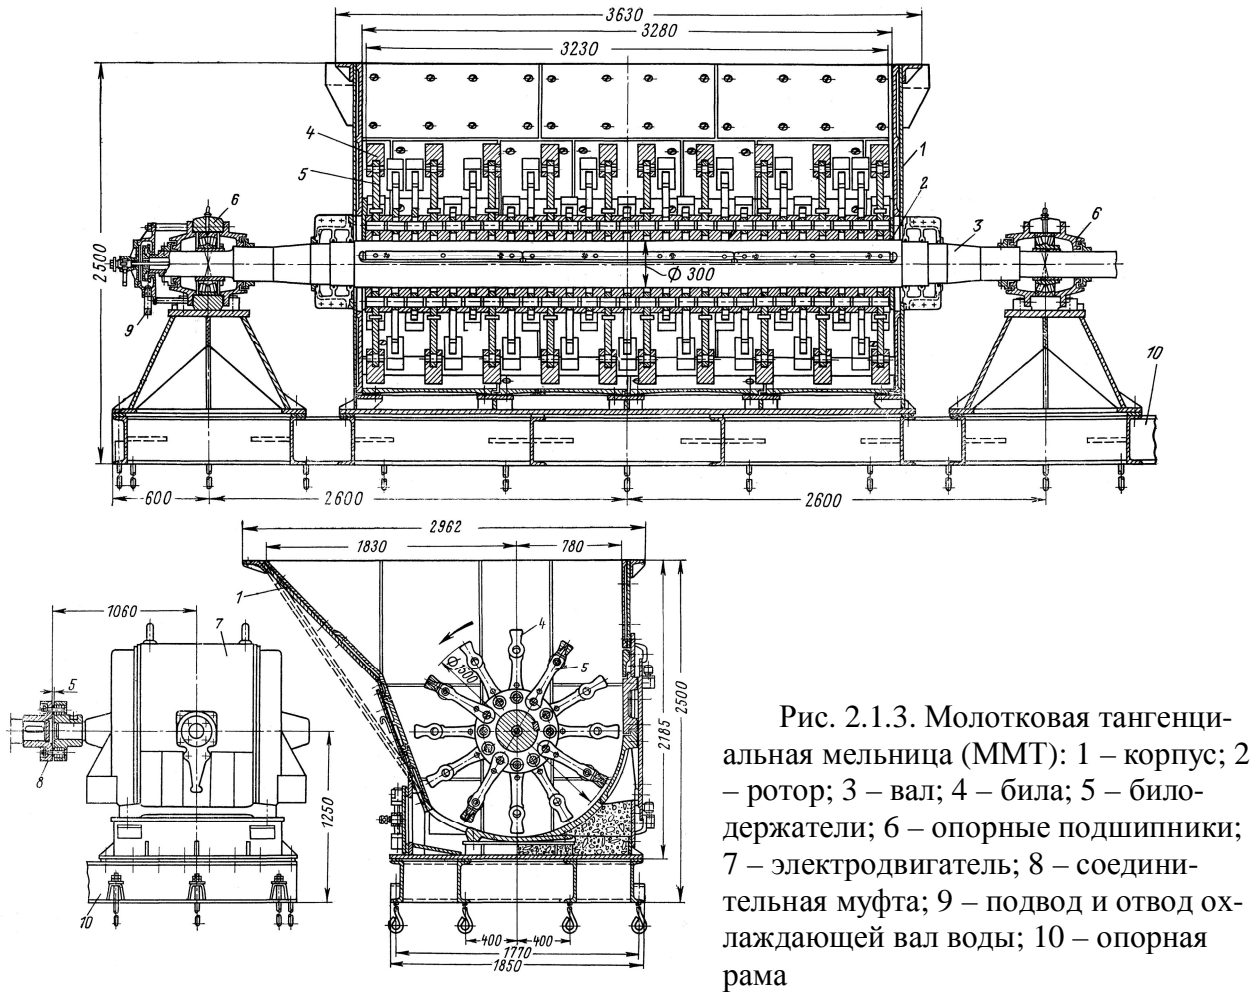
Молотковая тангенциальная мельница (ММТ): 1 – корпус; 2 – ротор; 3 – вал; 4 – била; 5 – билодержатели; 6 – опорные подшипники; 7 – электродвигатель; 8 – соединительная муфта; 9 – подвод и отвод охлаждающей вал воды; 10 – опорная рама
